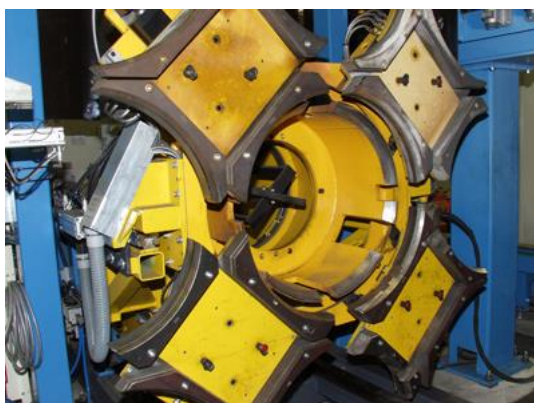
В то время как оператор устанавливает новые крышку и днище, роботы QIROX® затрачивают всего лишь 6 минут на сварку резервуара для горячей воды.
